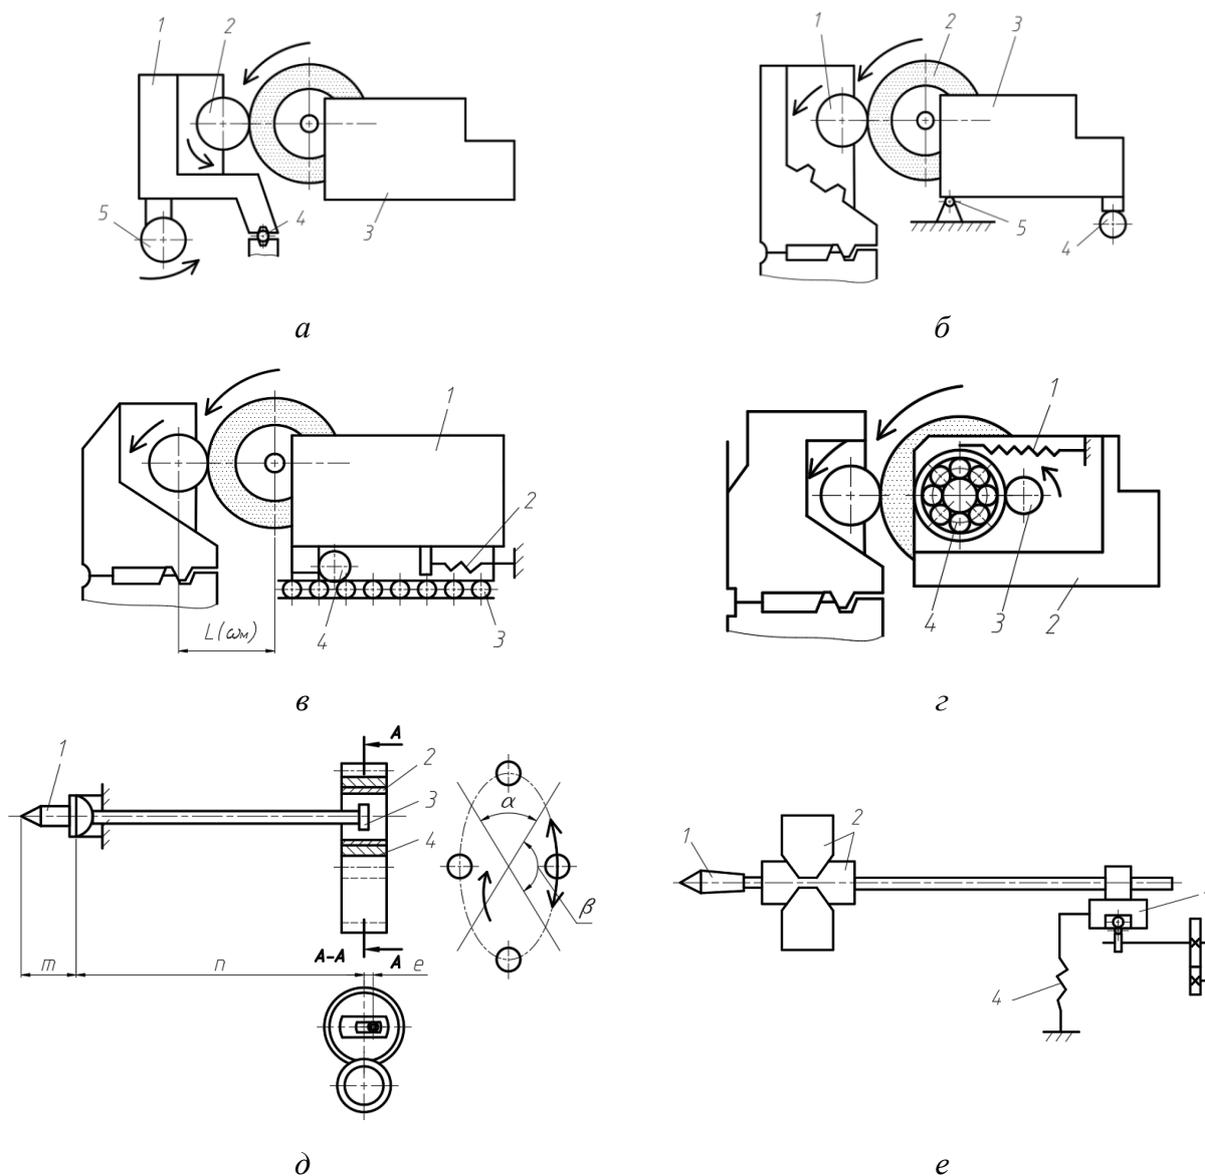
Схемы формообразующих движений в конструкциях резьбошлифовальных станков
